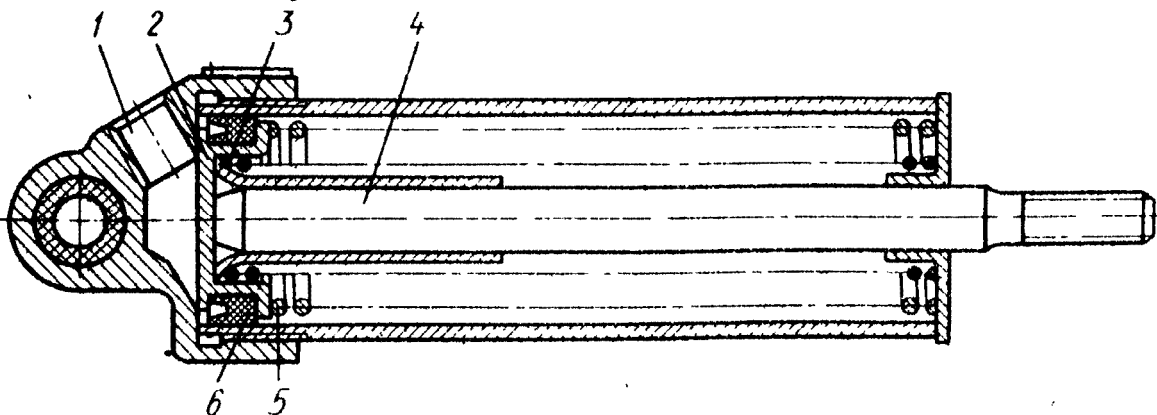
Пневматический цилиндр привода заслонки механизма вспомогательного тормоза:
